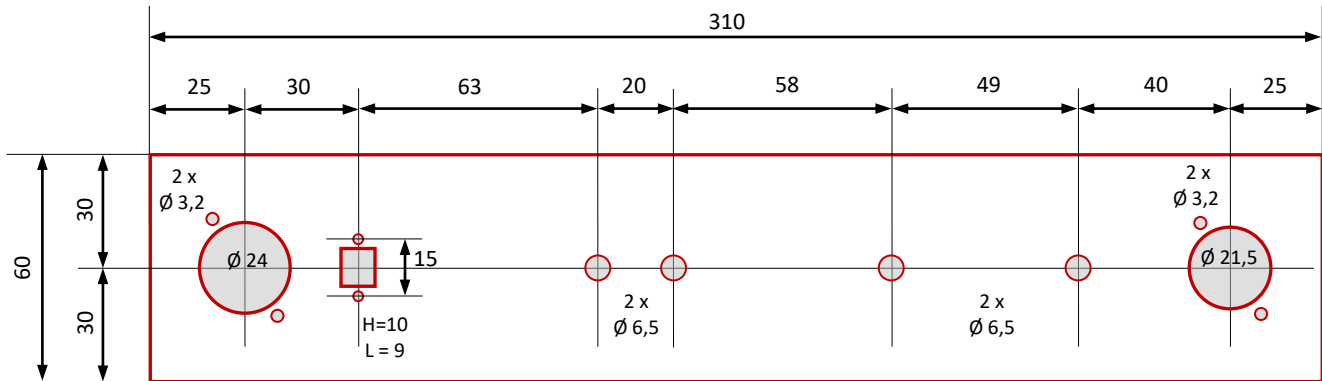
plan de l'usinage de la face arrière – Échelle ½
